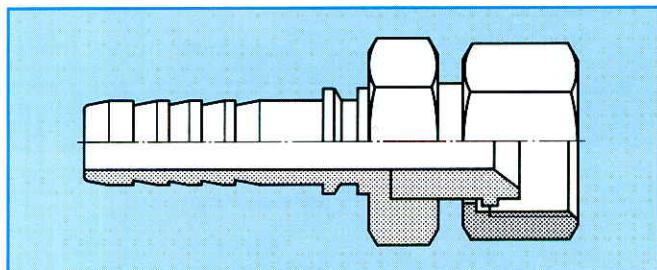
Прямой соединительный ниппель для резьбового соединения с уплотняющей отбортовкой
